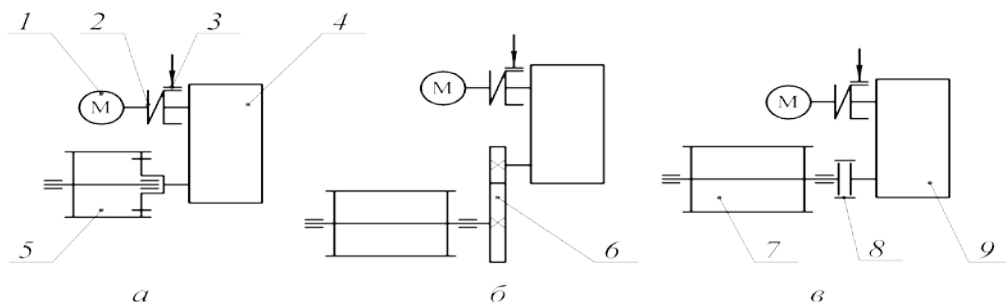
Кинематические схемы приводов механизма подъема:
